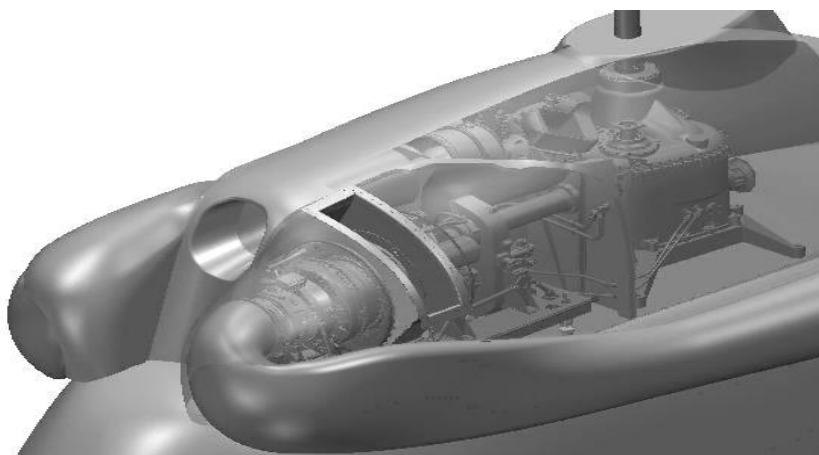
Компоновка двигательного отсека и главного редуктора
